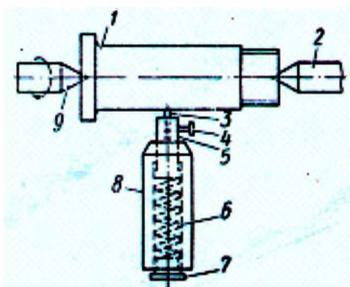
Схема фрикционного омеднения стальной детали: 1 – деталь, подвергающаяся меднению; 2 – подвижной центр задней бабки станка; 3 – медный пруток; 4 – винт для закрепления медного прутка; 5 – плунжер; 6 – пружина; 7 – резьбовая пробка; 8 – корпус приспособления, закрепленный в резцедержателе станка; 9 – центр, закрепленный в патроне
